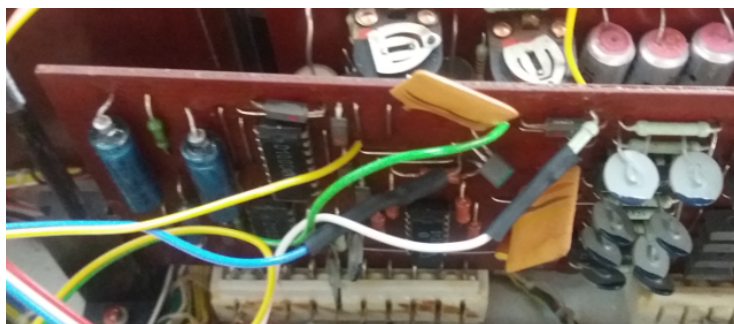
Detail PCB R12 po zaletování vodičů z přepínače
